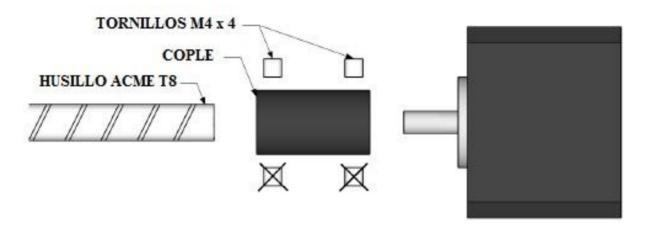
Unión de motor NEMA con husillo ACME T8 mediante cople.
